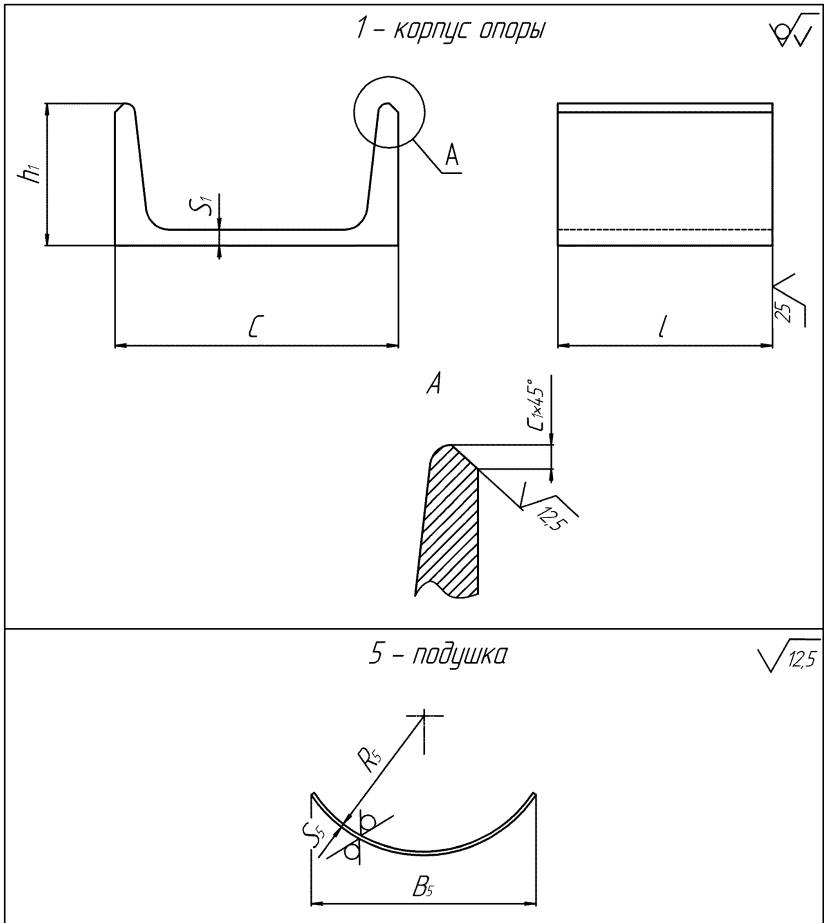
Детали изделий 02-XXXX-S-1C-XX-C,
